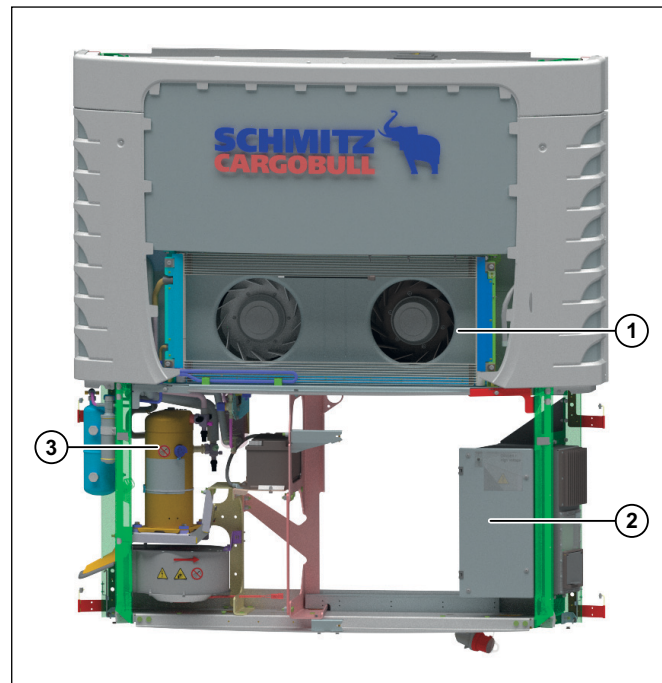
Вид з відчиненими дверима (S.CU e80)
